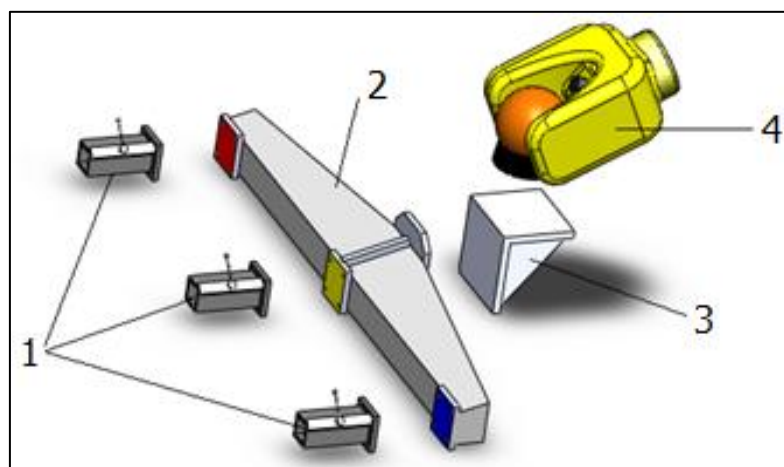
Vista Explodida dos Dispositivos Acoplados ao Robô
